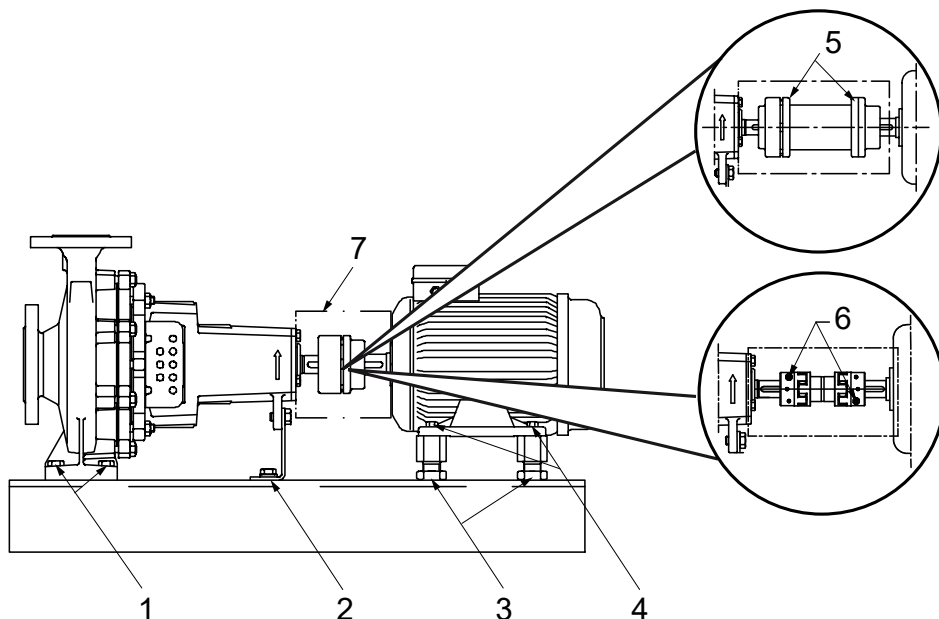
Místa pro utažení šroubů s průměry oběžného kola 250, kromě 065-050-200, 080-065-200, 100-080-200
